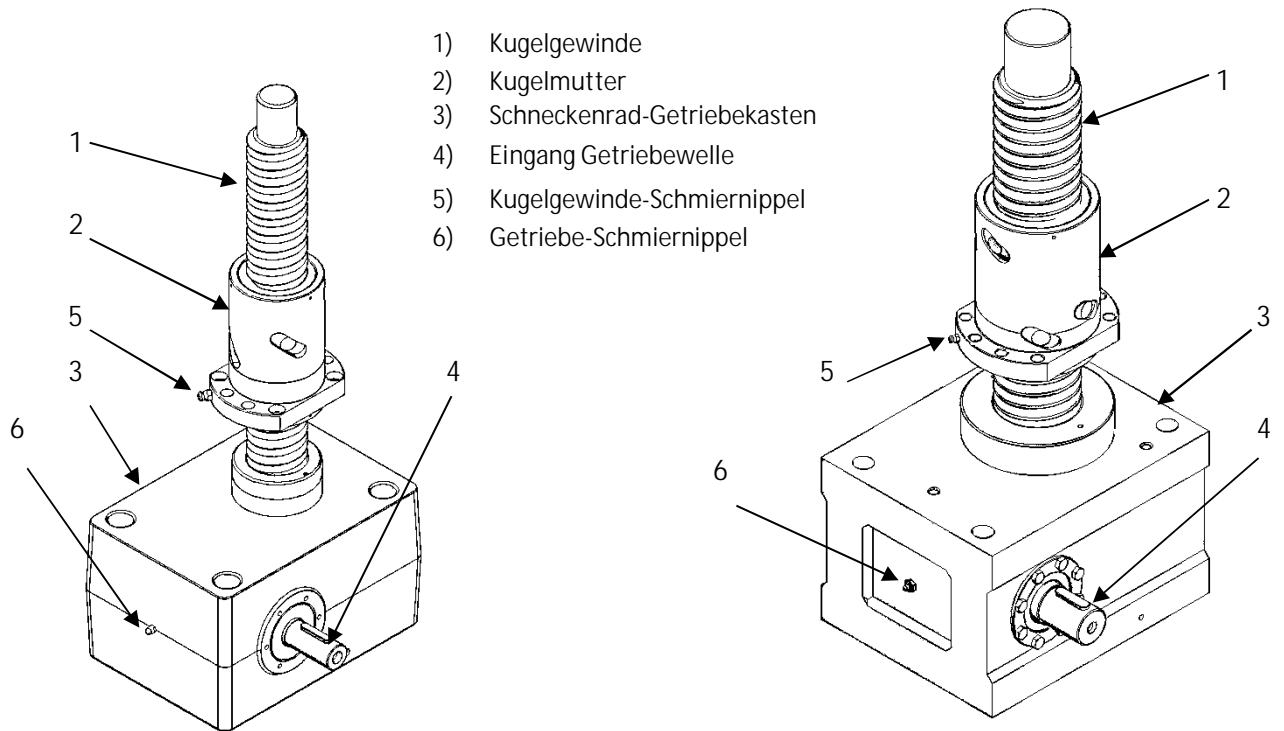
Hauptkomponenten des MA BS Mod.B Kugelgewinde-Hubgetriebes
